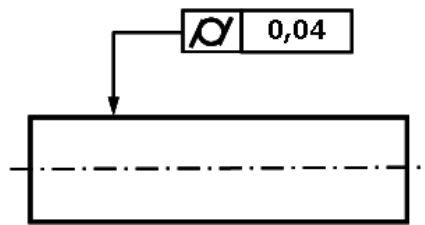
Indicação de Tolerância de Cilindridade em desenho técnico
